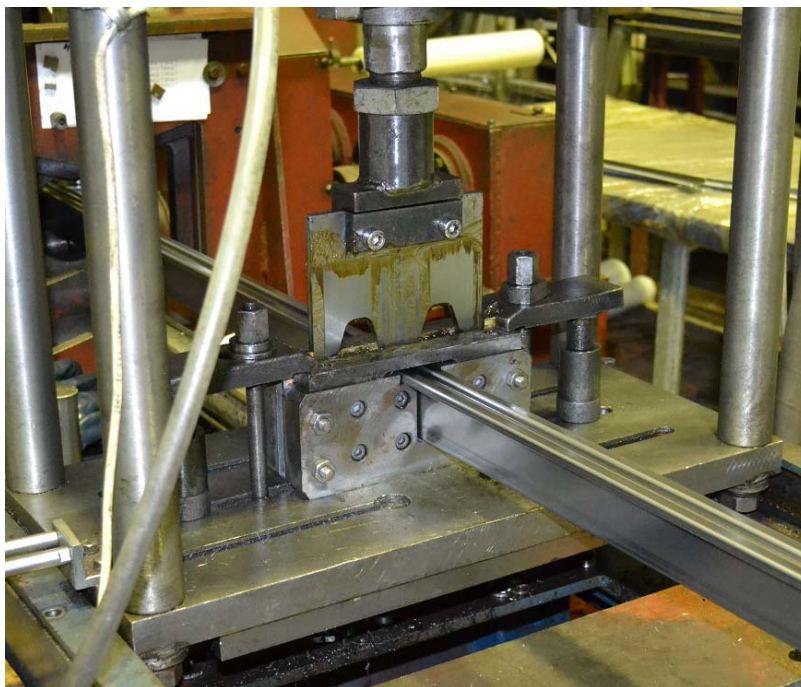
Общий вид отрубного устройства со стандартным типом штампа
